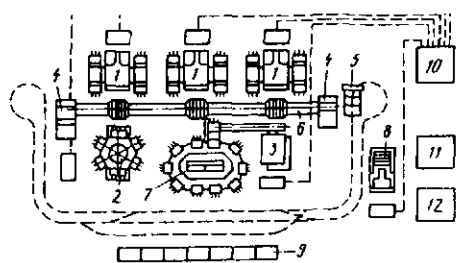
Гибкая автоматизированная линия со станками с ЧПУ, оснащенными многошпиндельными головками: 1 – 3 – станки с ЧПУ с устройствами автоматической смены многошпиндельных головок; 4 – позиции загрузки-разгрузки заготовок; 5 – робокара; 6 – конвейер заготовок (палет с заготовками); 7 – накопитель многошпиндельных головок; 8 – контрольно-измерительная машина с ЧПУ; 9 – позиция накопления заготовок; 10 – центральная ЭВМ; 11 – ЭВМ управления транспортом; 12 – ЭВМ управления контролем и настройкой инструмента
